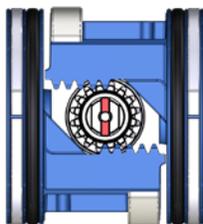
Исполнение С – Приводы закрывающие против часовой стрелке, верхний вал перпендикулярно корпусу
